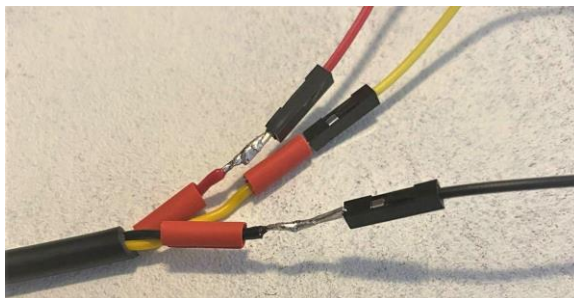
Detall de la soldadura dels cables amb el tub termoretràctil abans d'escalfar per ajustar a la posició.
